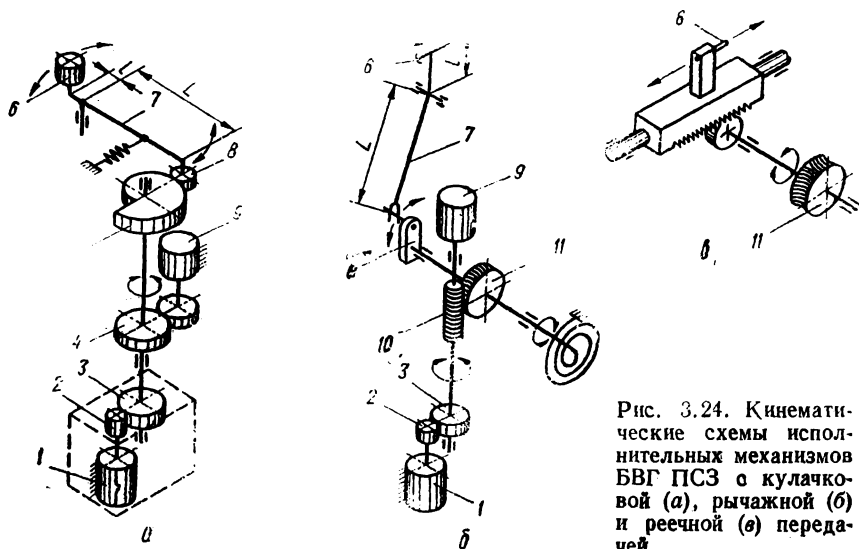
Кинематические схемы исполнительных механизмов БВГ ПСЗ с кулачковой (а), рычажной (б) и реечной (в) передачей
